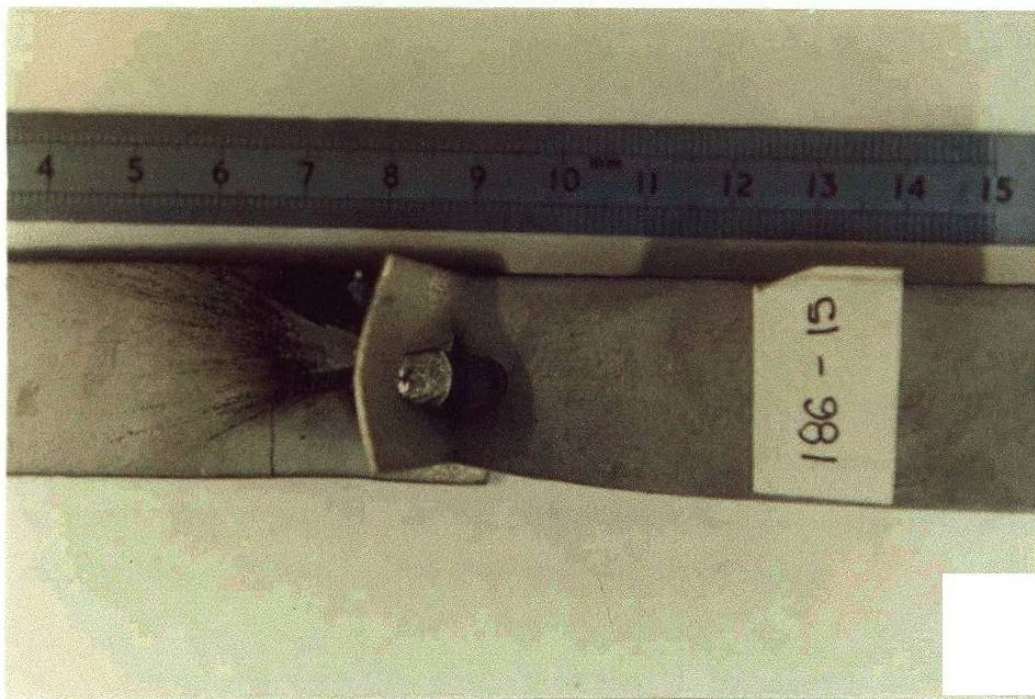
Probeta de tensión de la muestra A soldada con 10.28 kA.
